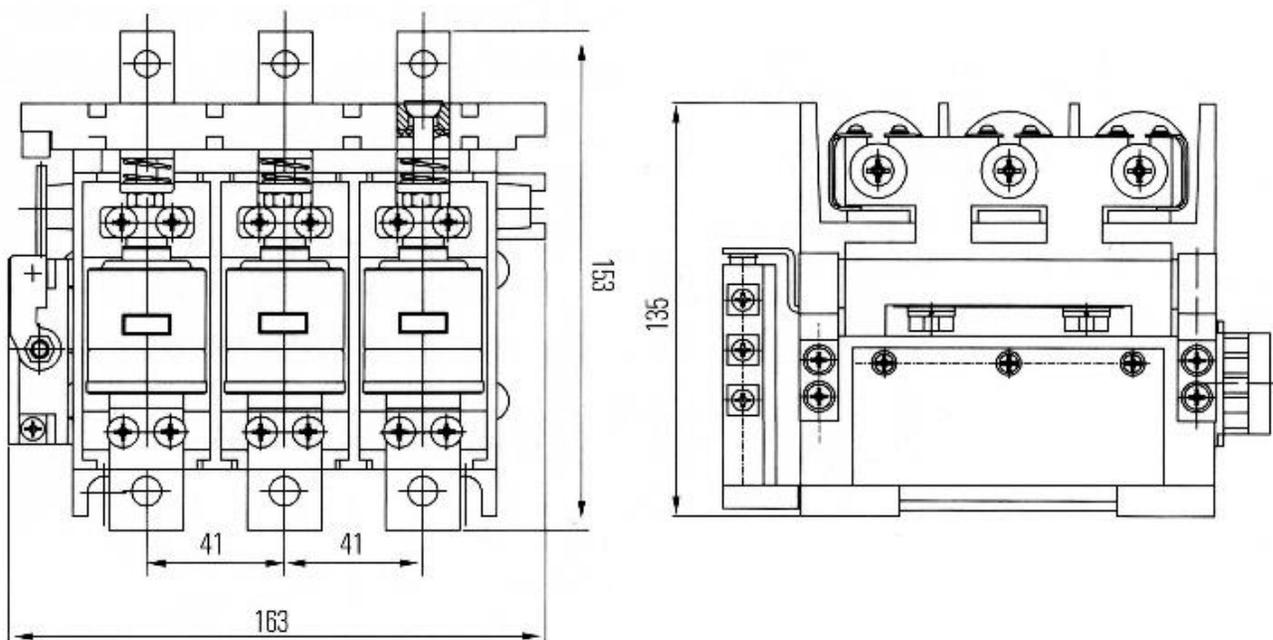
Габаритные размеры KBT-1,14-80/125/160
